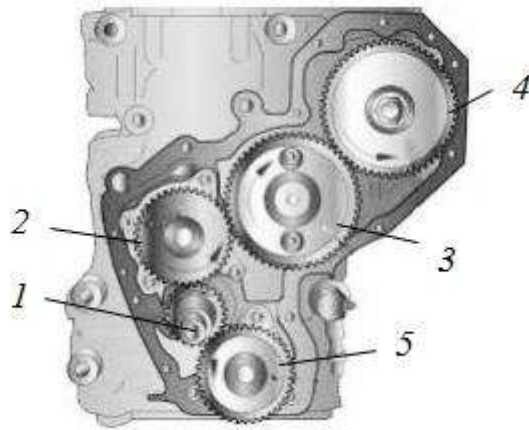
Шестеренчастий привод розподільчого валу:
